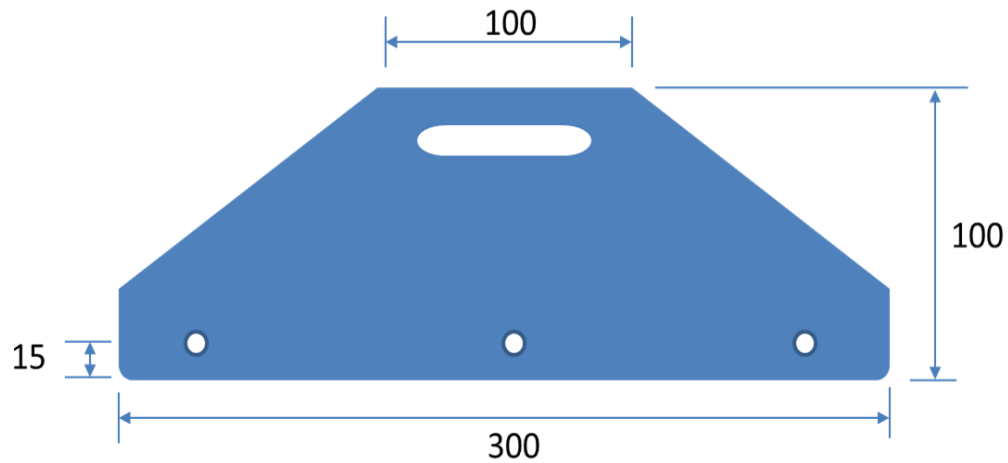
Dimensiones de la placa superior de sostén. Fuente: Propia
